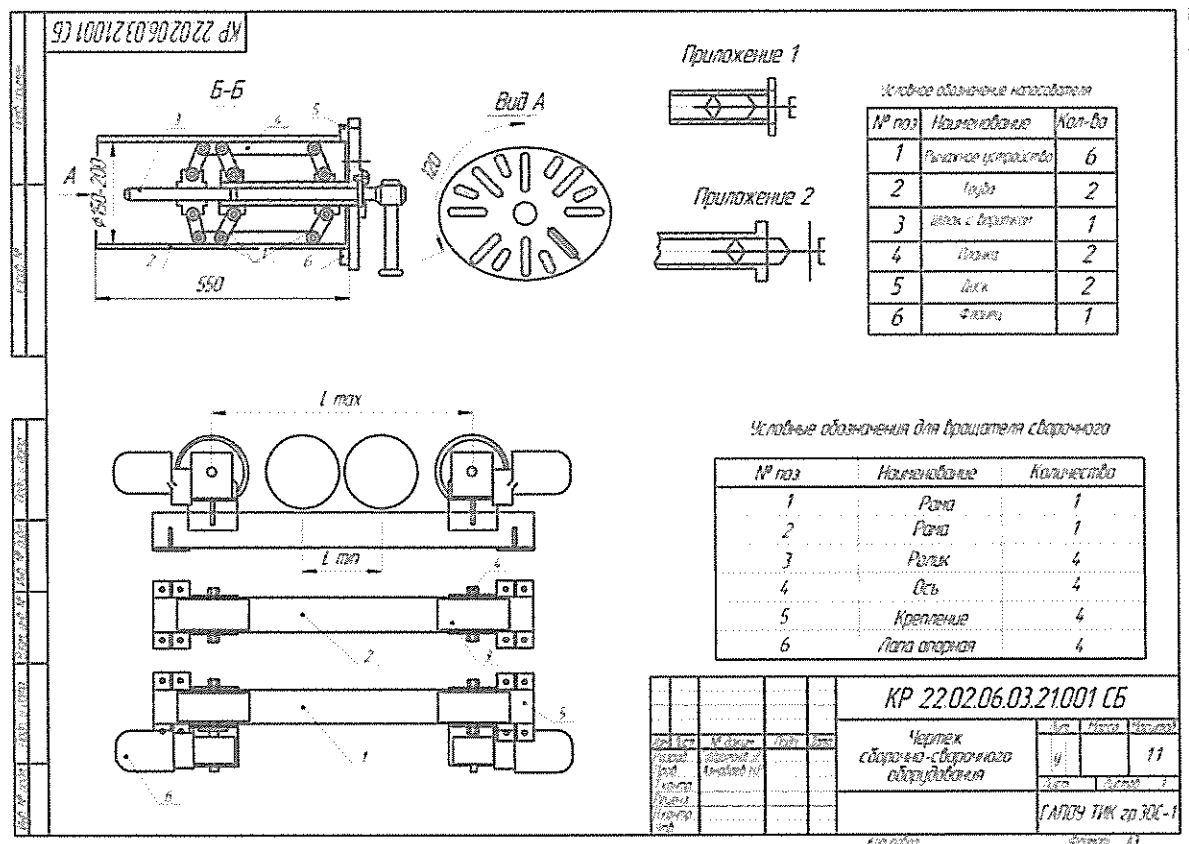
Образец чертежа сборочно – сварочного оборудования
